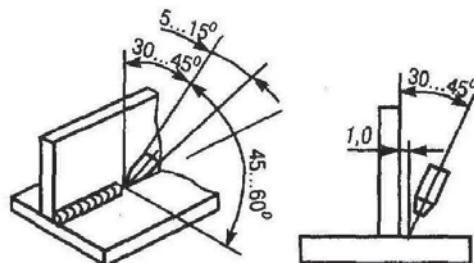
Положение горелки при механизированной сварке угловых швов
